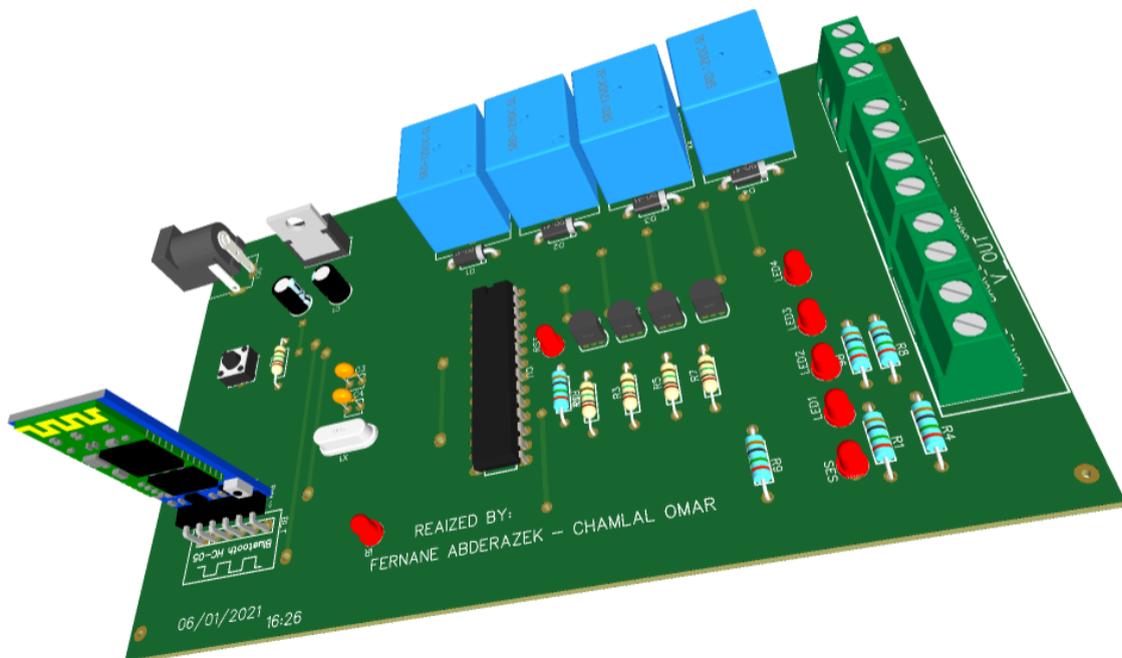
Carte PCB en 3 Dimensions 'Coté Gauche'
